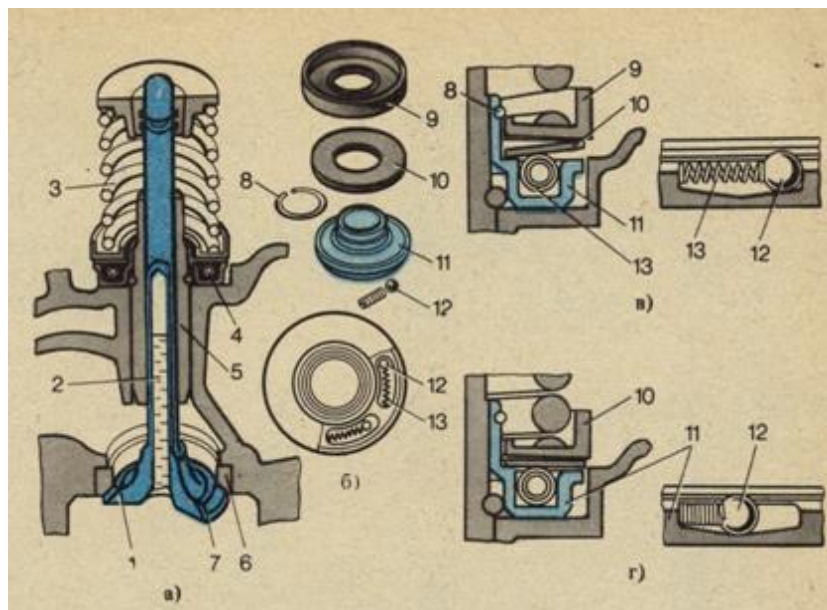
Клапанный механизм автомобильного двигателя: а - выпускной клапан с механизмом вращения в сборе, б - механизм вращения, в - положение механизма при закрытом клапане, г - положение механизма при открытом клапане; 1 - тарелка клапана, 2 - полость, 3 - пружина клапана, 4 - механизм вращения, 5 - втулка клапана, 6 - седло клапана, 7 - рабочая фаска, 8 - замочное кольцо, 9 - упорная шайба, 10 - дисковая пружина, 11 - корпус механизма вращения, 12 - шарик, 13 - возвратная пружина.
